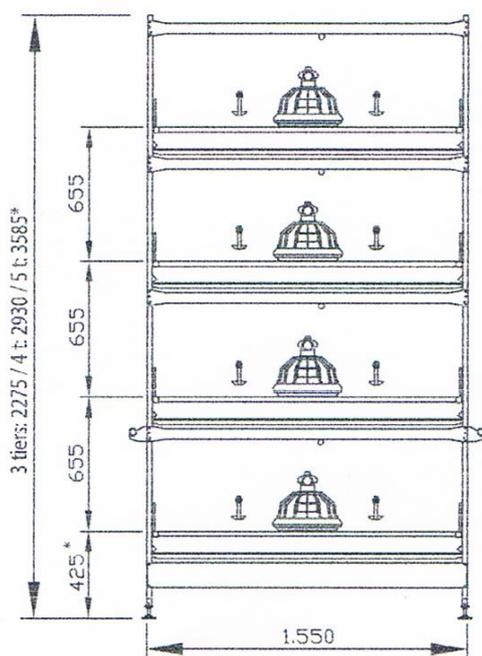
Dimensions et disposition des batteries d'élevage du poulet de chair.
